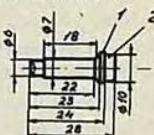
Палец вала управления коробкой передач с противошумным стержнем.
